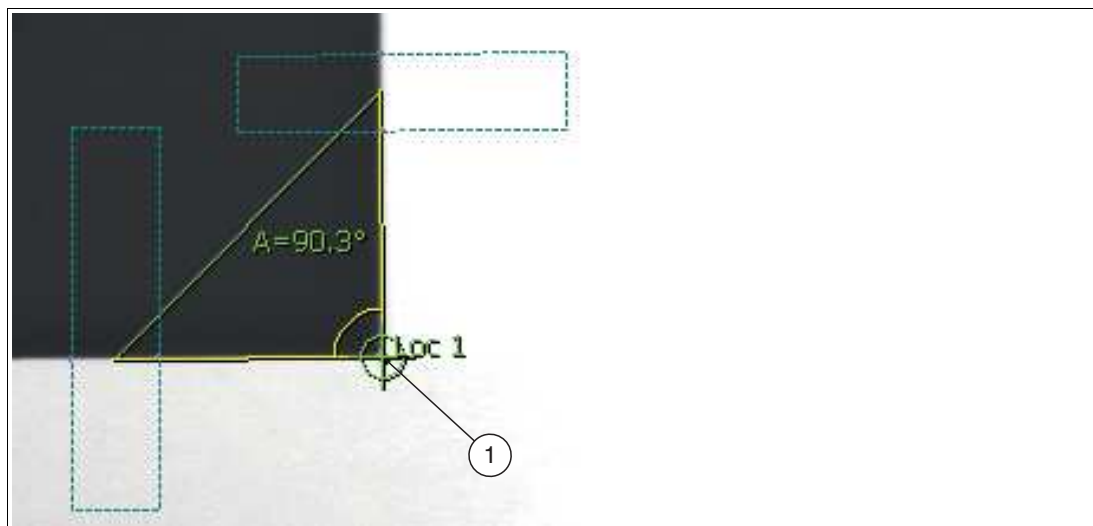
Referenzpunkt zum Ausrichten weiterer Werkzeuge
